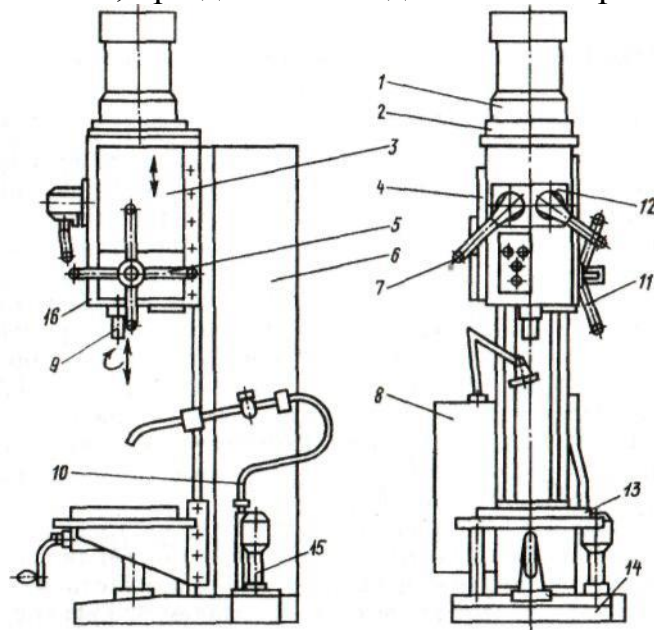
Общий вид вертикально-сверлильного станка мод. 2Н135:
